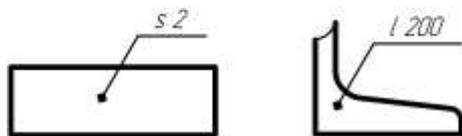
Нанесение на полке линии выноски толщины детали и длины детали
